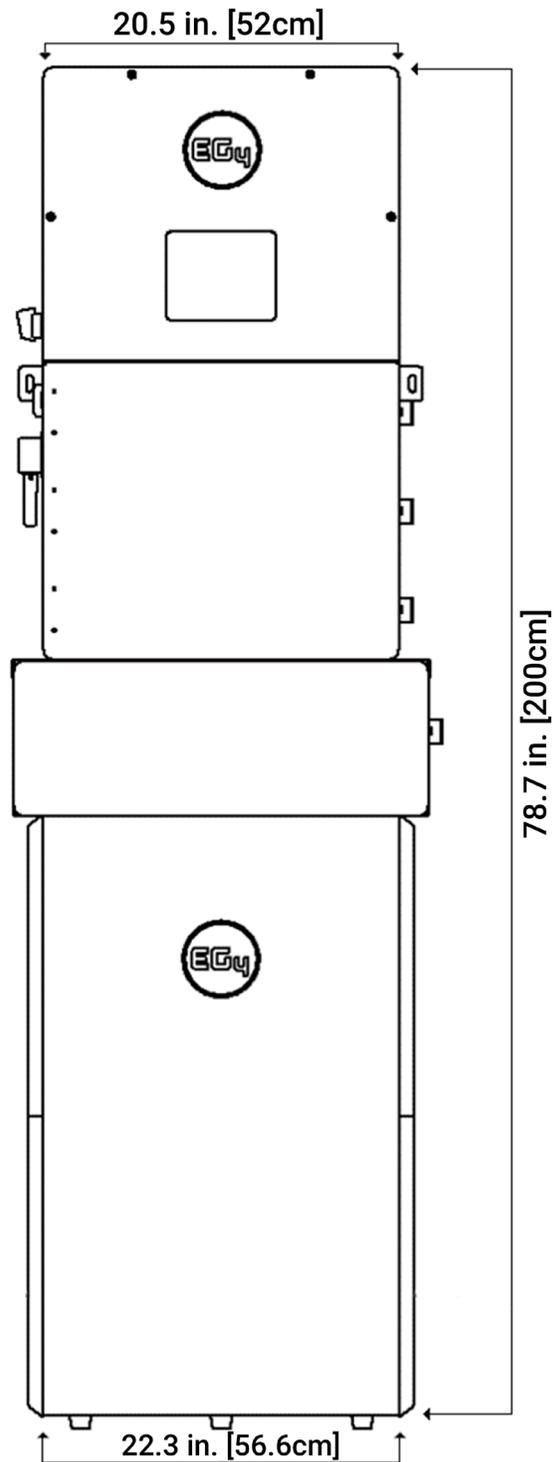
WallMount Instalación con Caja de Conductor y 18kPV Final
